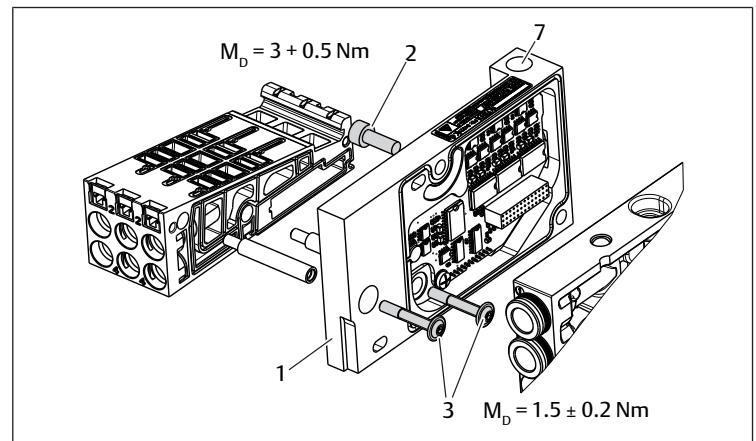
Monte el módulo adaptador AV05-B-Design en una placa base AV05
